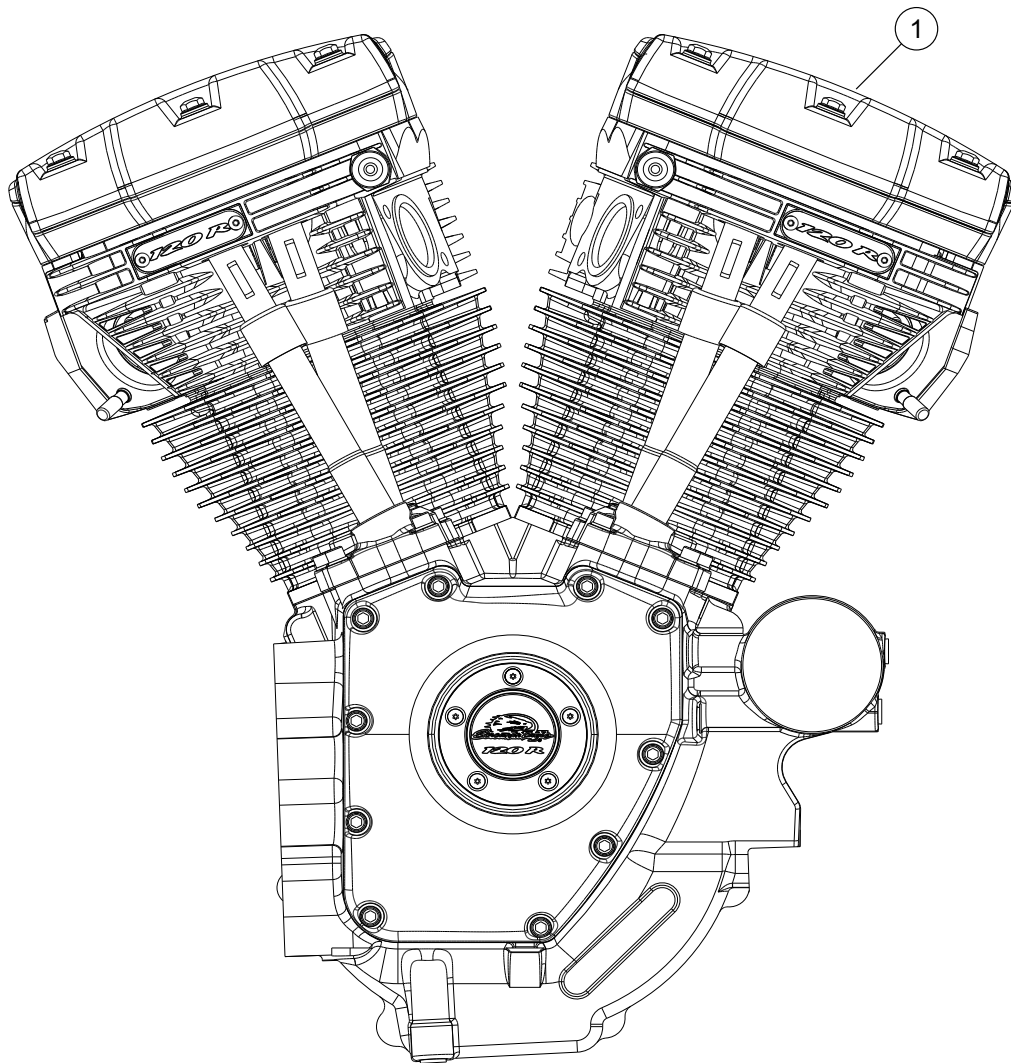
Assemblage du moteur, moteur en caisse (Alpha) SE Pro 120R complet
